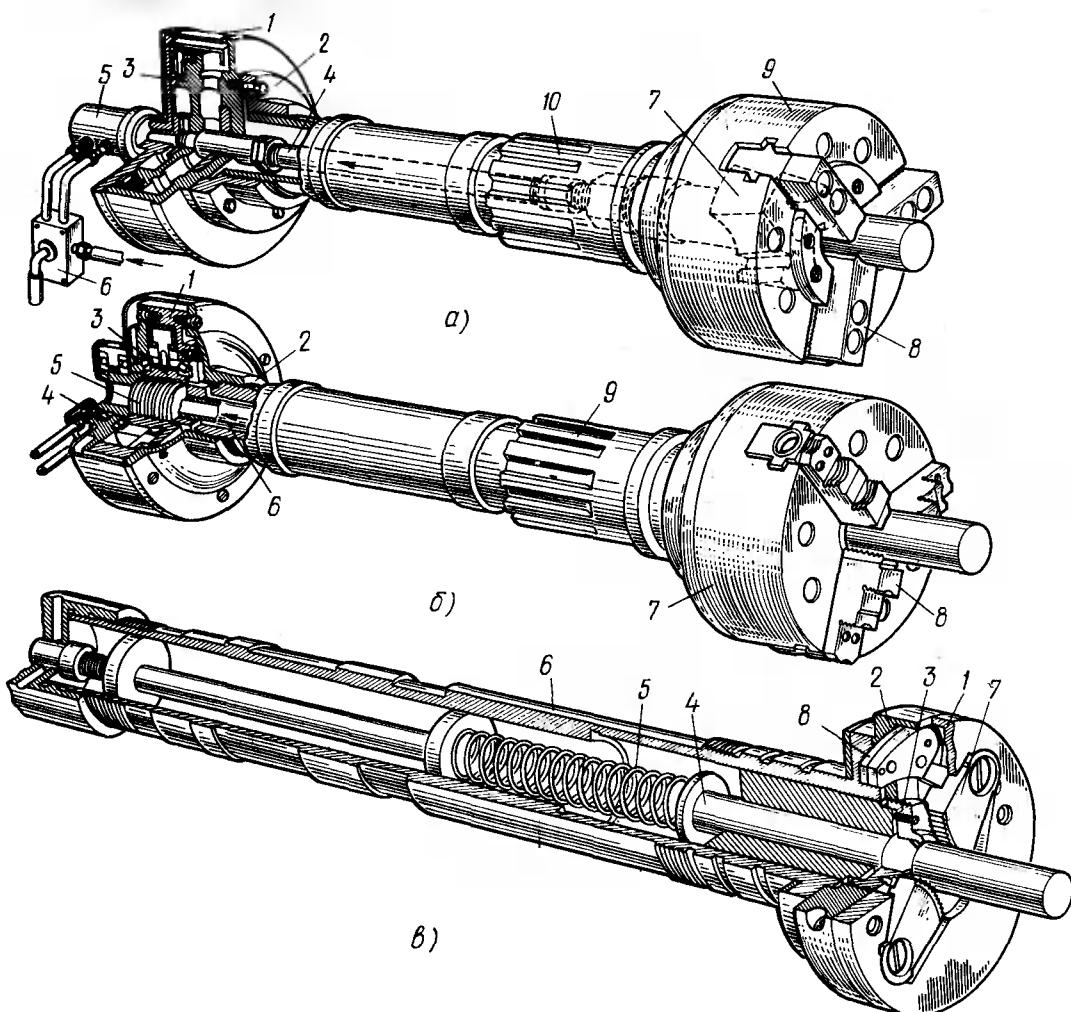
Патроны, применяемые для закрепления заготовок:
